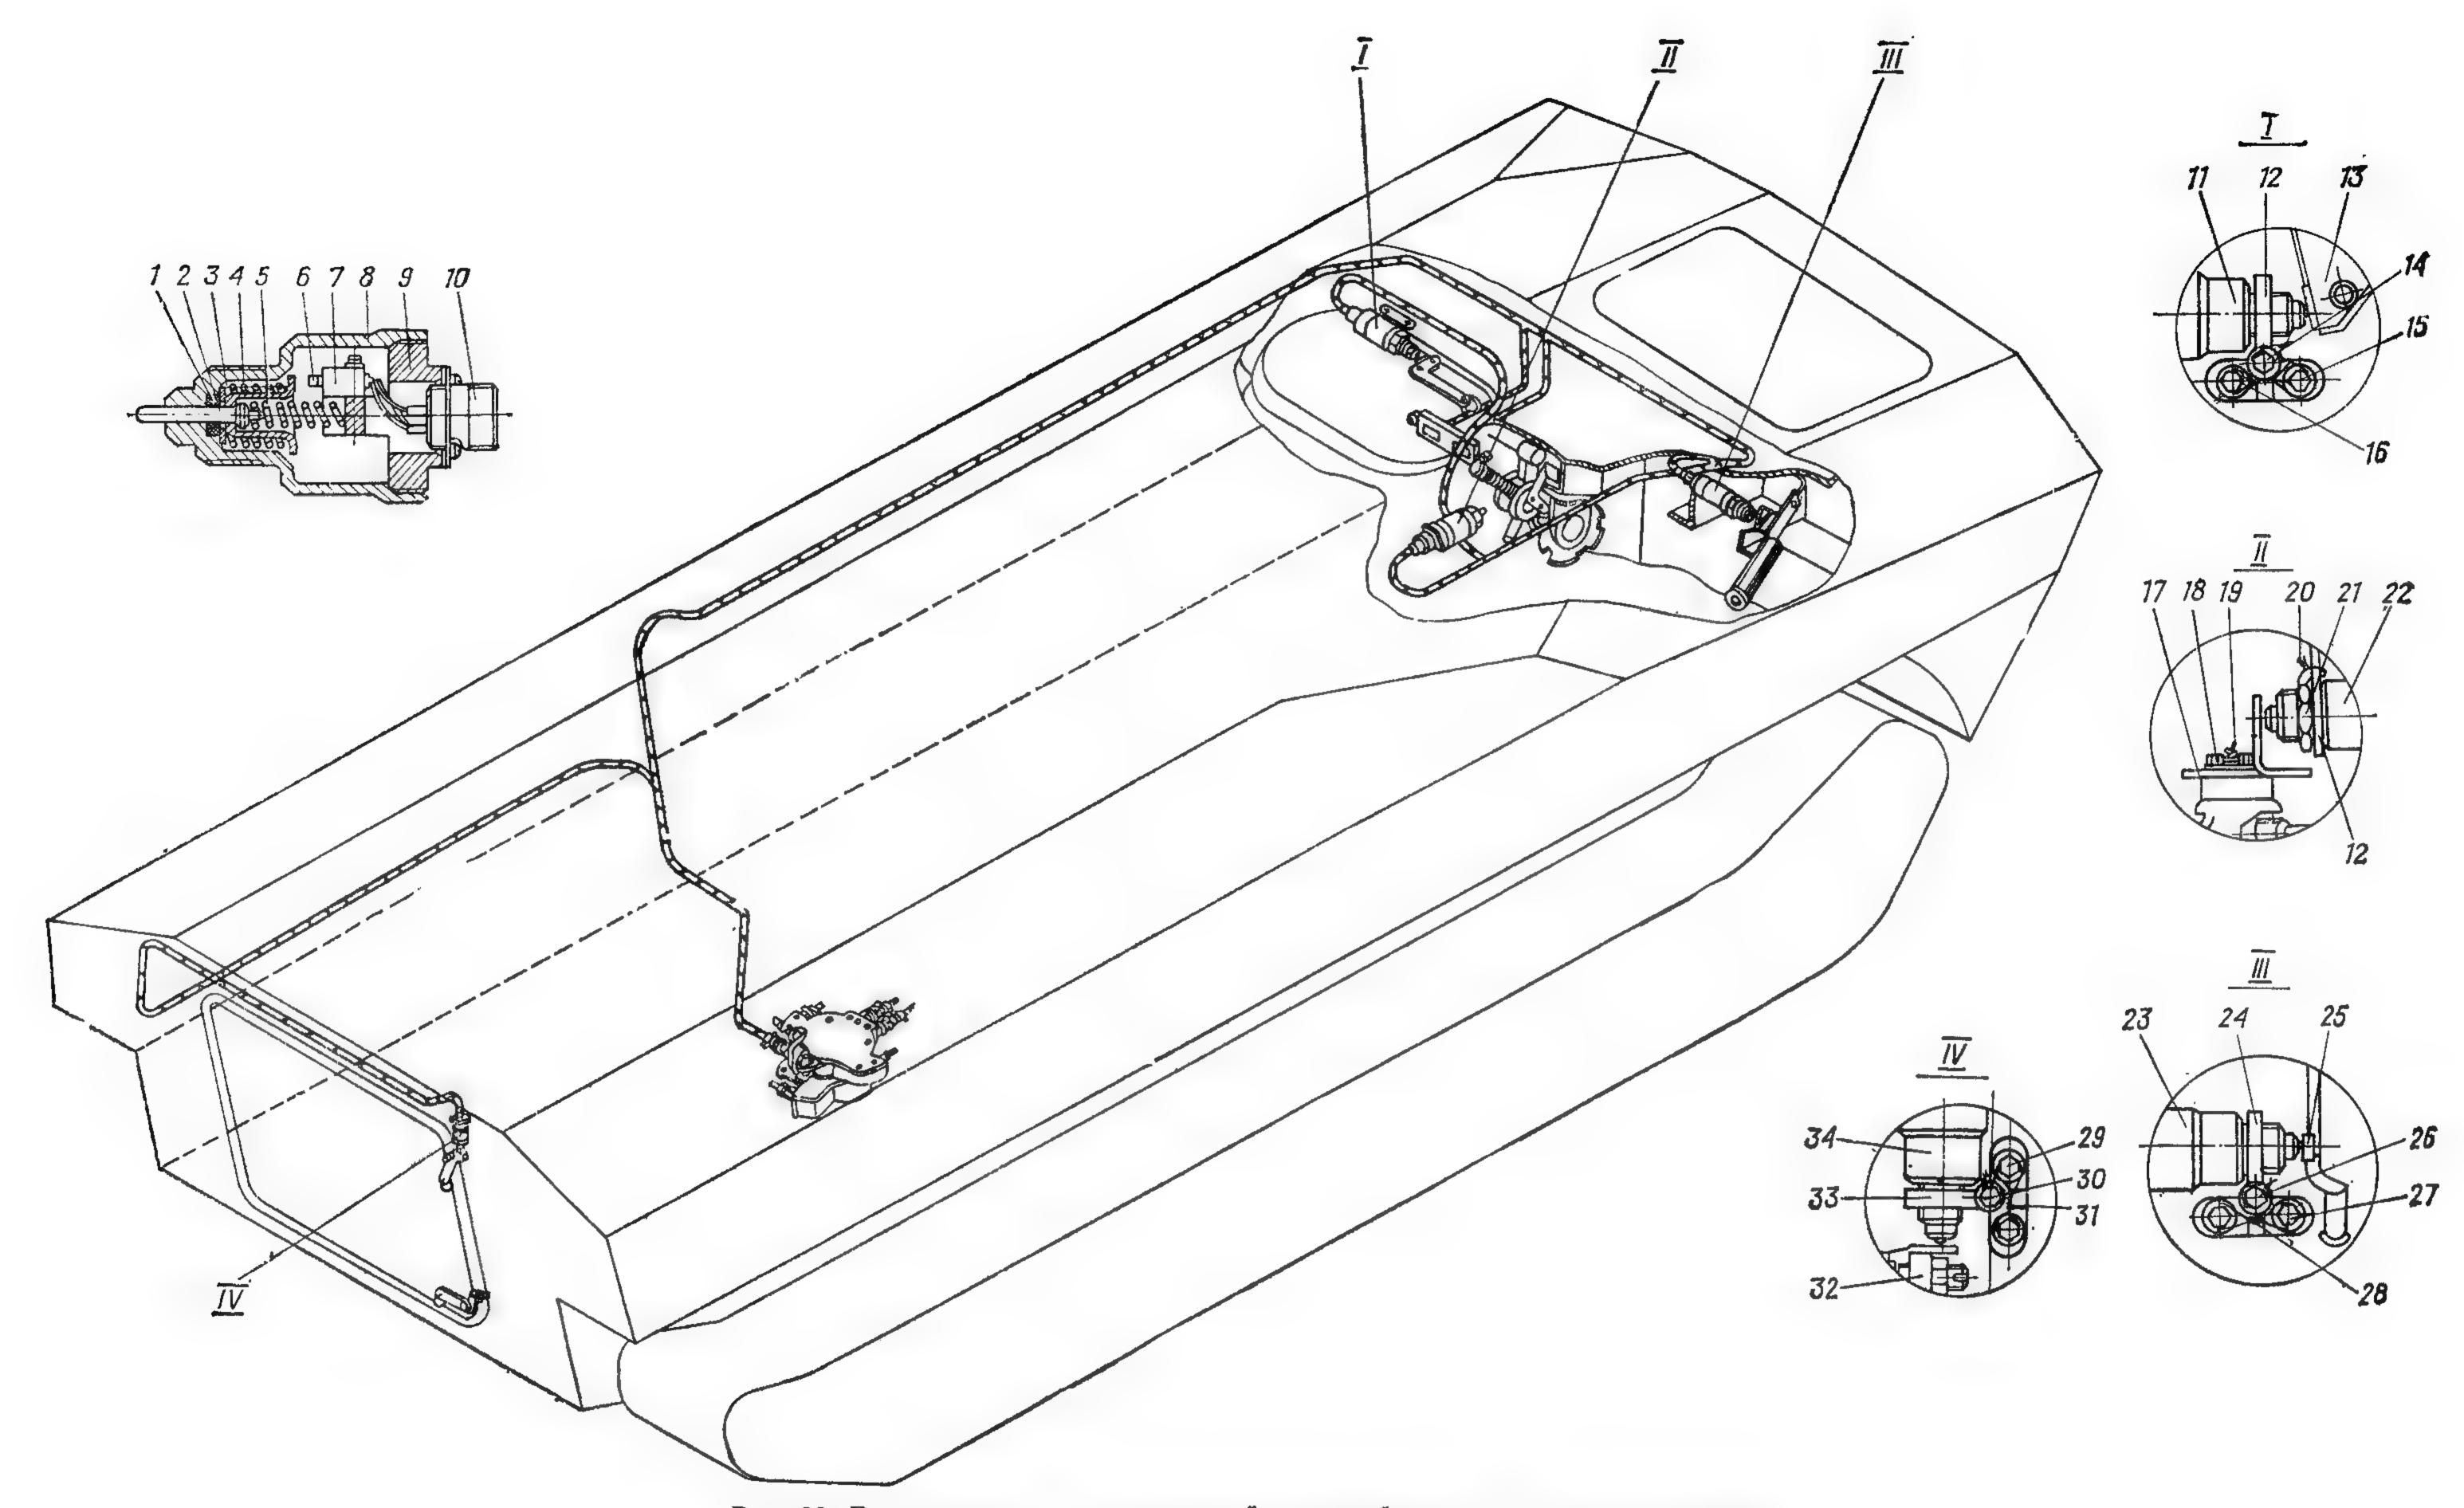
Расположение переключателей электроблокировок в корпусе шасси: 1—уплотнитель; 2—шток; 3—стакан; 4, 5—пружина; 6—шток микропереключателя; 7—микропереключатель; 8—корпус; 9—крышка; 10—вилка; 11—переключатель крышки люка механика-водителя; 12—17, 24, 33—кронштейны; 13, 32—рычаги; 14, 15, 18, 26, 27, 29, 30—болты; 16, 19, 20, 28, 31—проволоки; 21—гайка; 22—переключатель щитка смотрового стекла механика-водителя; 23—переключатель стопора ствола; 34—переключатель; 23—переключатель кормового люка
